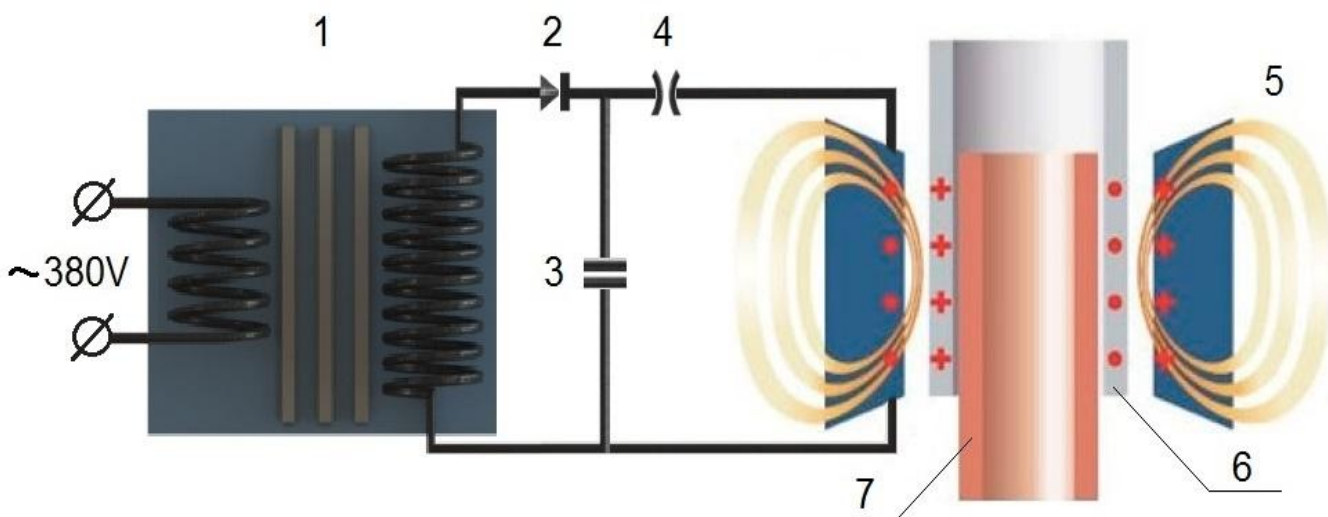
Схема магнитно-импульсной сварки: 1 – повышающий трансформатор, 2 – выпрямительное устройство, 3 – импульсные конденсаторы, 4 – разрядное устройство, 5 – индуктор, 6 – деформируемая трубчатая заготовка, 7 – соединяемая с деформируемой заготовкой внутренняя труба
